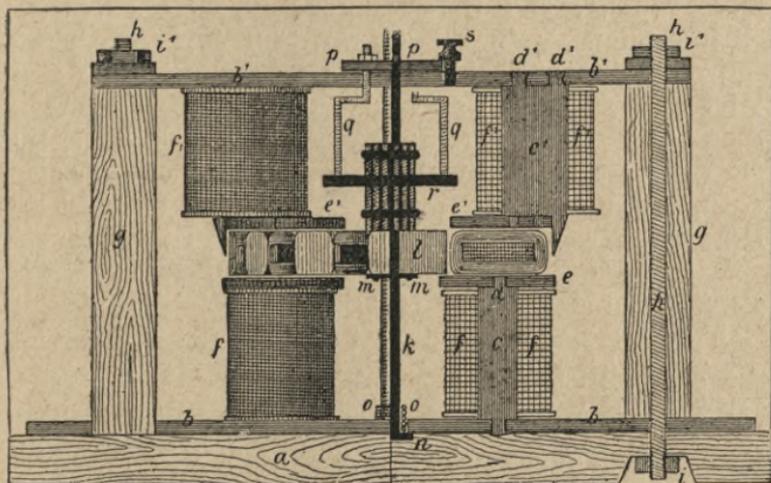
Fertiger Motor (links Ansicht, rechts Schnitt).
